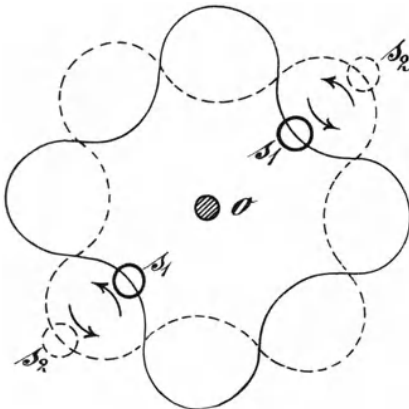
a. Das Prinzip der Umklöppelmaschinen.
